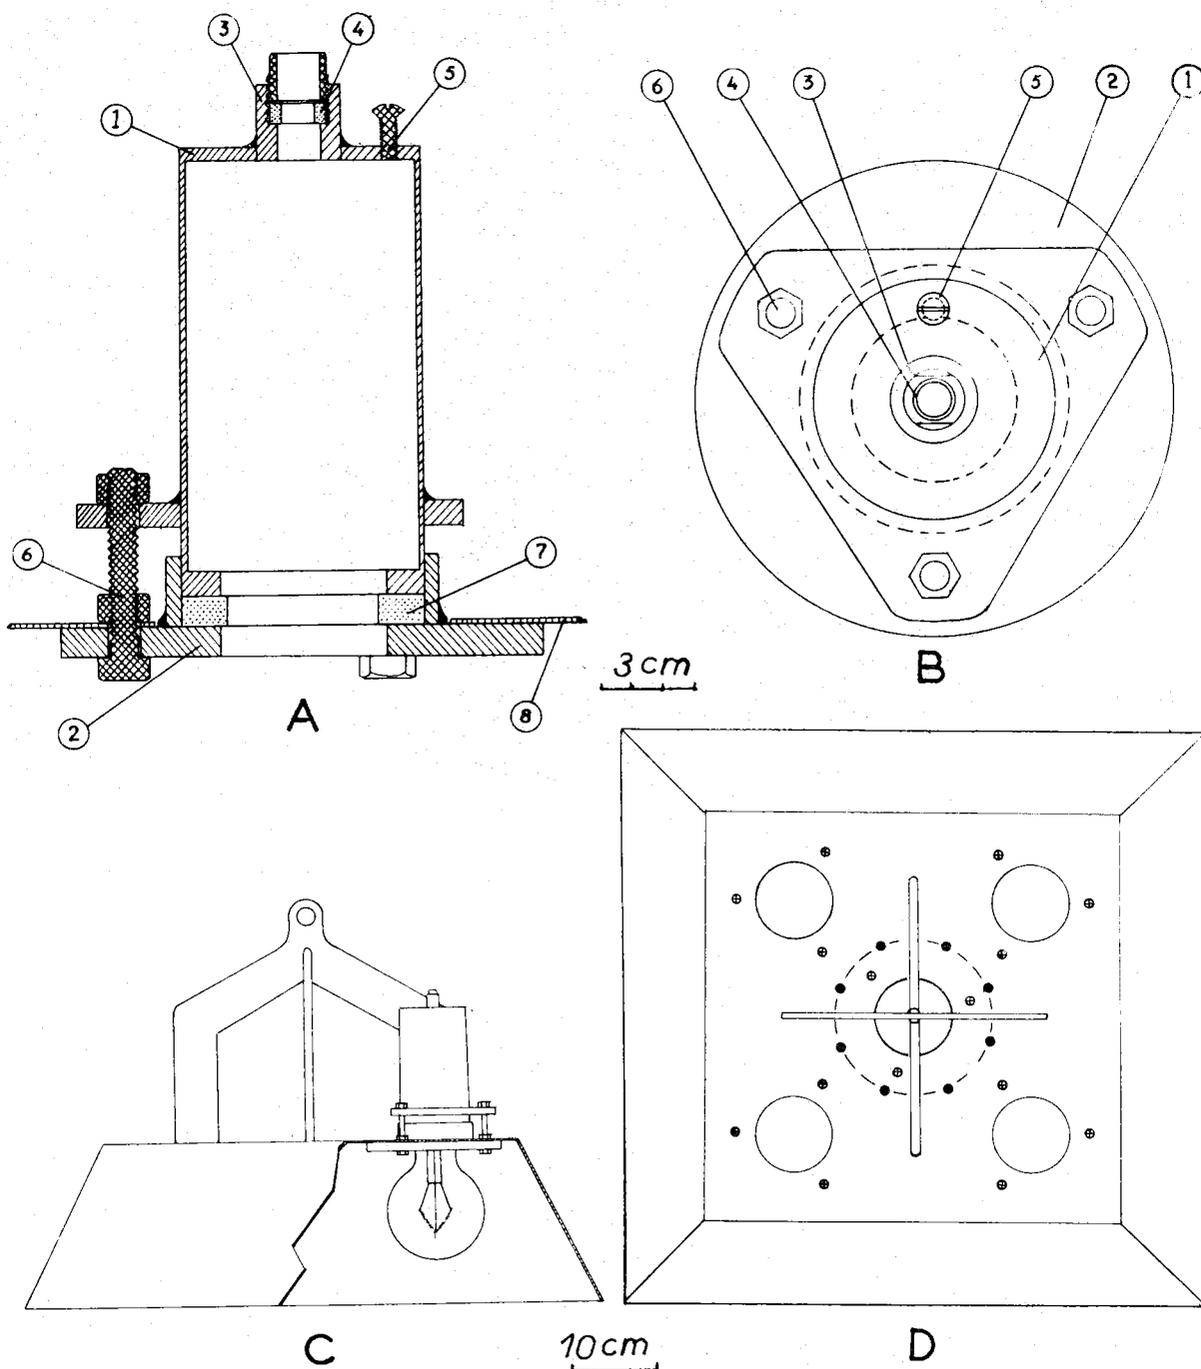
Lampe de pêche immergeable du type ISTPM. A et B : coupe et plan d'une douille étanche. Les chiffres entourés d'un cercle désignent : 1 corps de la douille ; 2 collier de serrage sur l'ampoule ; 3 presse-étoupe du câble électrique ; 4 joint d'étanchéité en caoutchouc sur le câble ; 5 orifice de remplissage d'huile ; 6 boulon de fixation de la douille sur le réflecteur ; 7 joint d'étanchéité en caoutchouc sur le col de l'ampoule ; 8 tôle du réflecteur. C et D : coupe et plan d'un réflecteur à 5 ampoules. Les petits cercles représentent les orifices de circulation d'eau, les points noirs sont les passages des boulons de fixation des douilles sur le réflecteur (figure déjà publiée dans « Science et Pêche » n° 69/70, 1959).
